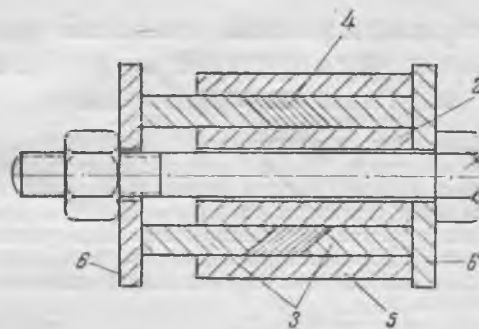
Прессформа для изготовления самоуплотняющейся набивки.
